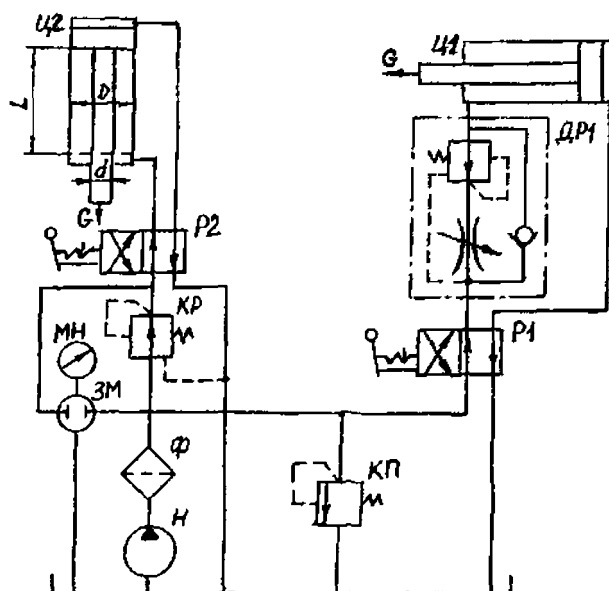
Гидропривод подачи стола фрезерного станка
